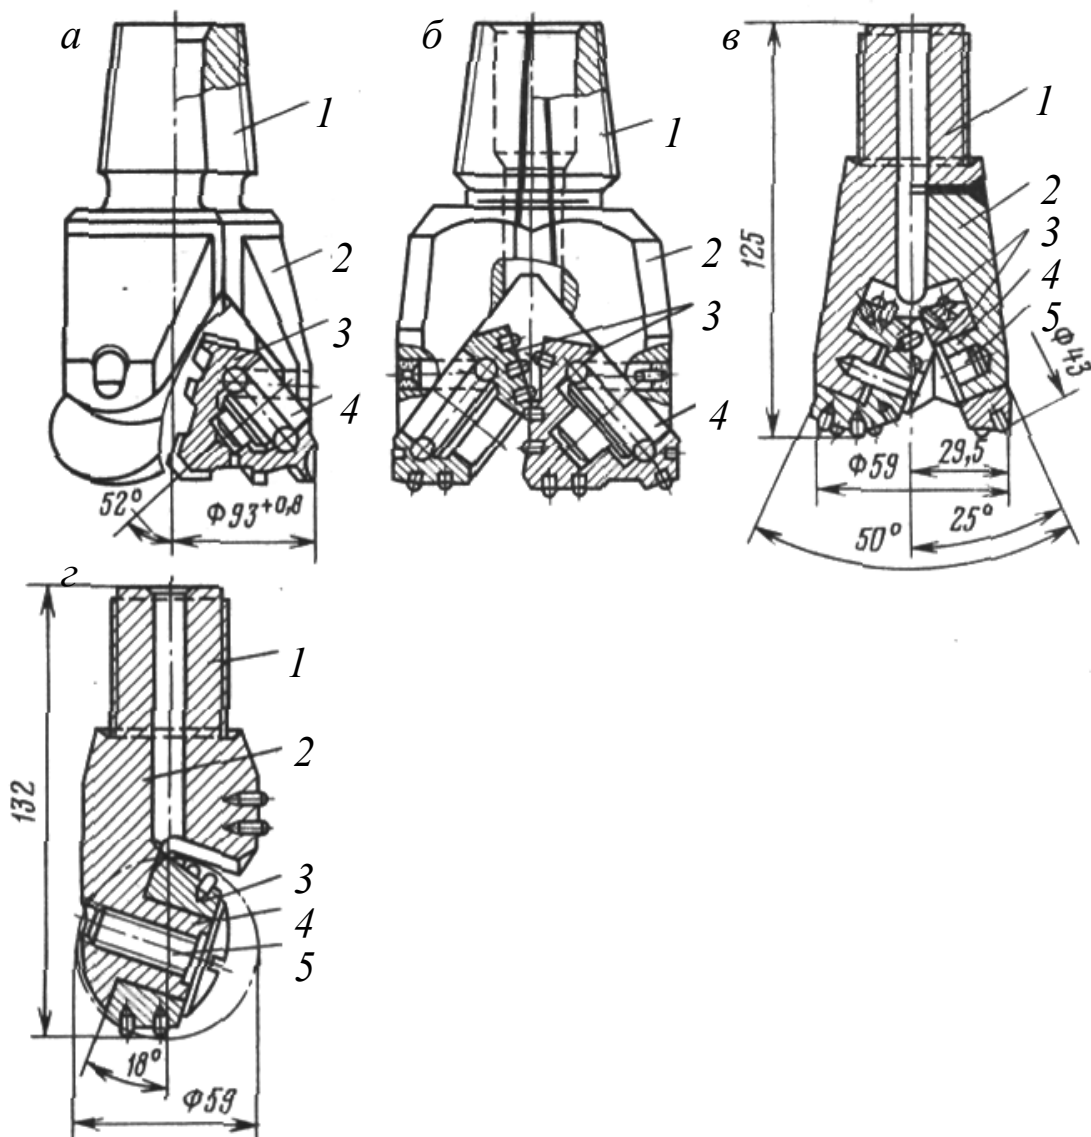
Конструкции шарошечных долот для бурения в твердых породах: 1 – присоединительная резьба; 2 – лапа; 3 – шарошки; 4 – цапфа; 5 – запорный палец с буртиком
